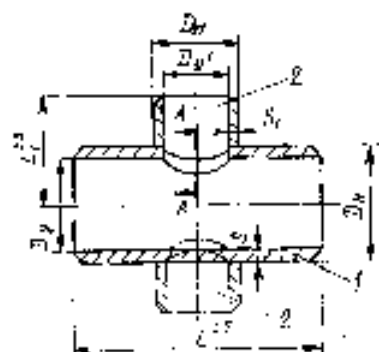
Тройник (фитинг) переходной сварной
